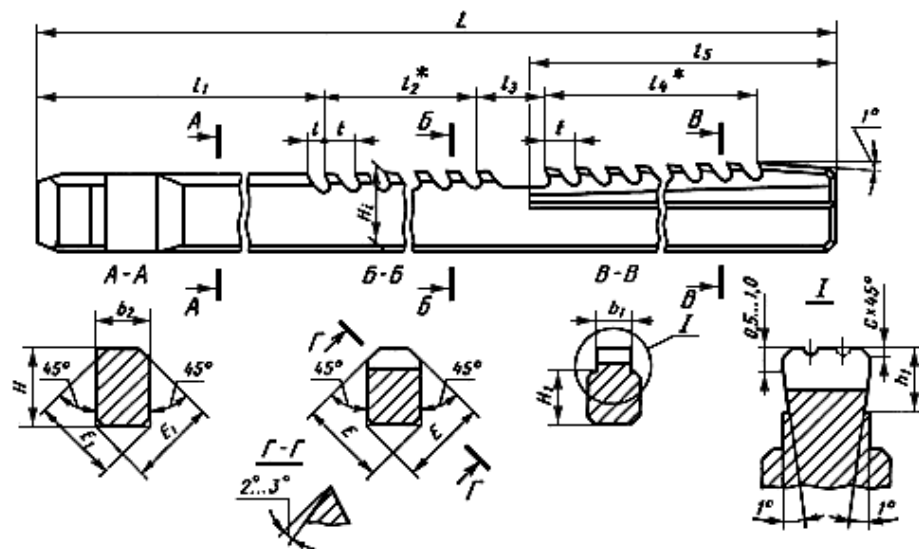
Основні конструктивні розміри робочого інструменту для протягування шпонкового пазу (шпонкової протяжки)
